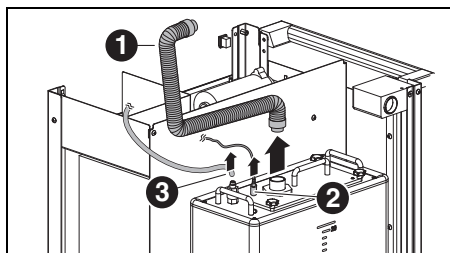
Desserrer les interfaces de l'unité d'alimentation
